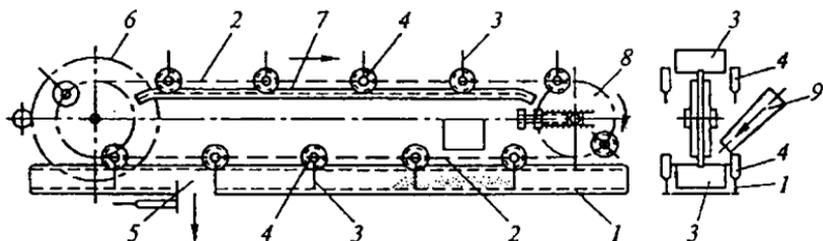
Схема скребкового транспортера: 1 — неподвижный желоб; 2 — цепь; 3 — скребок; 4 — ролик; 5 — разгрузочное отверстие; 6 — приводная звездочка; 7 — направляющие; 8 — натяжная звездочка; 9 — лоток
